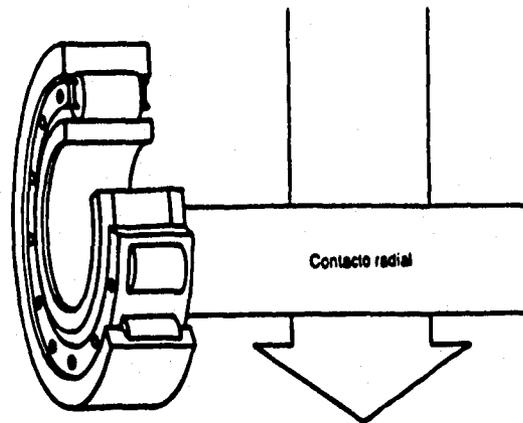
Rodamiento de rodillos cilíndricos.
